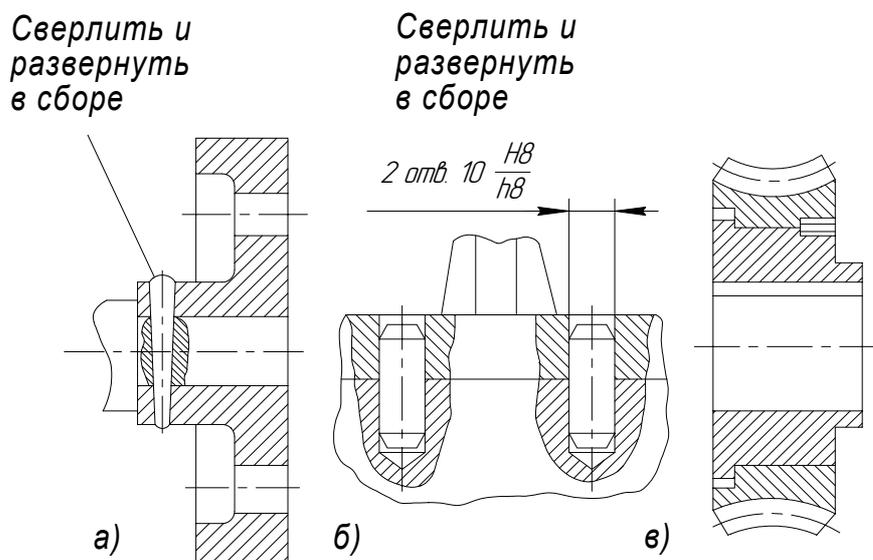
Соединения, требующие совместного сверления отверстий при сборке
